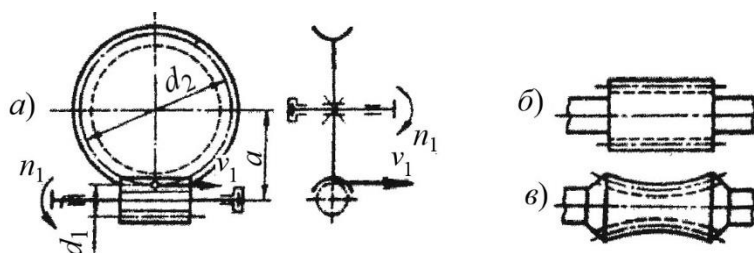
Схема червячной передачи лифтового редуктора:
